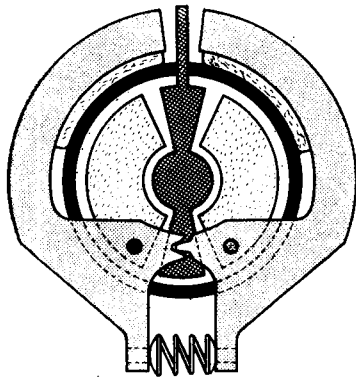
a. Motorspærren. Motoren i Staa. Bremseklodserne trykker paa Bremsetromlen.
